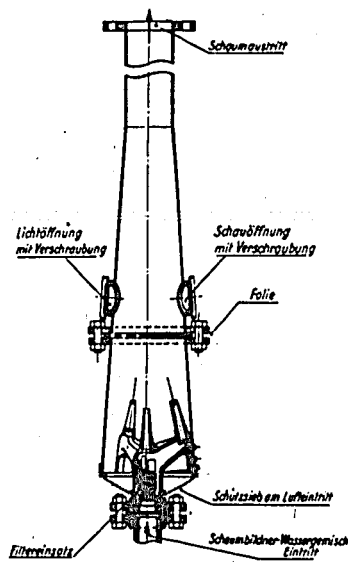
Tankkometrohr mit Folie und Schaulöffnungen — Tube comète pour réservoir, avec feuille et regards — Tank comet pipe with foil and inspection holes
